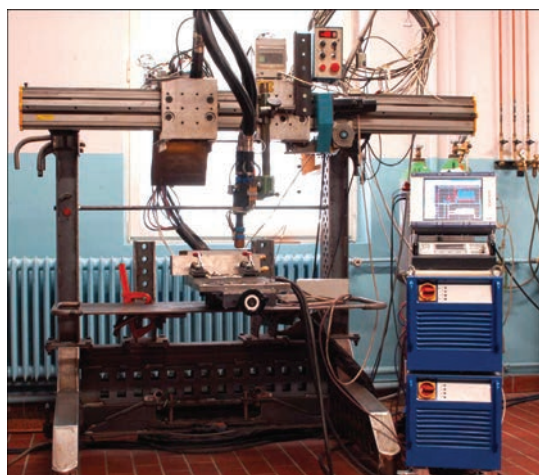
Установка Hybrid 8000 MR для гибридной плазменно-дуговой сварки плавящимся электродом с аксиальной подачей электродной проволоки фирмы АМТ Maschinen- und Gerätetechnik GmbH (ФРГ)
